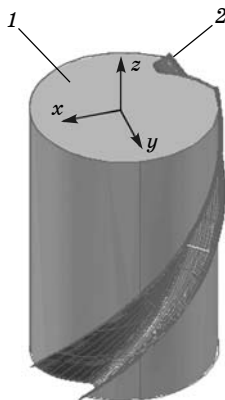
Модель тела с винтовой канавкой 1 и цилиндрической винтовой поверхностью 2
